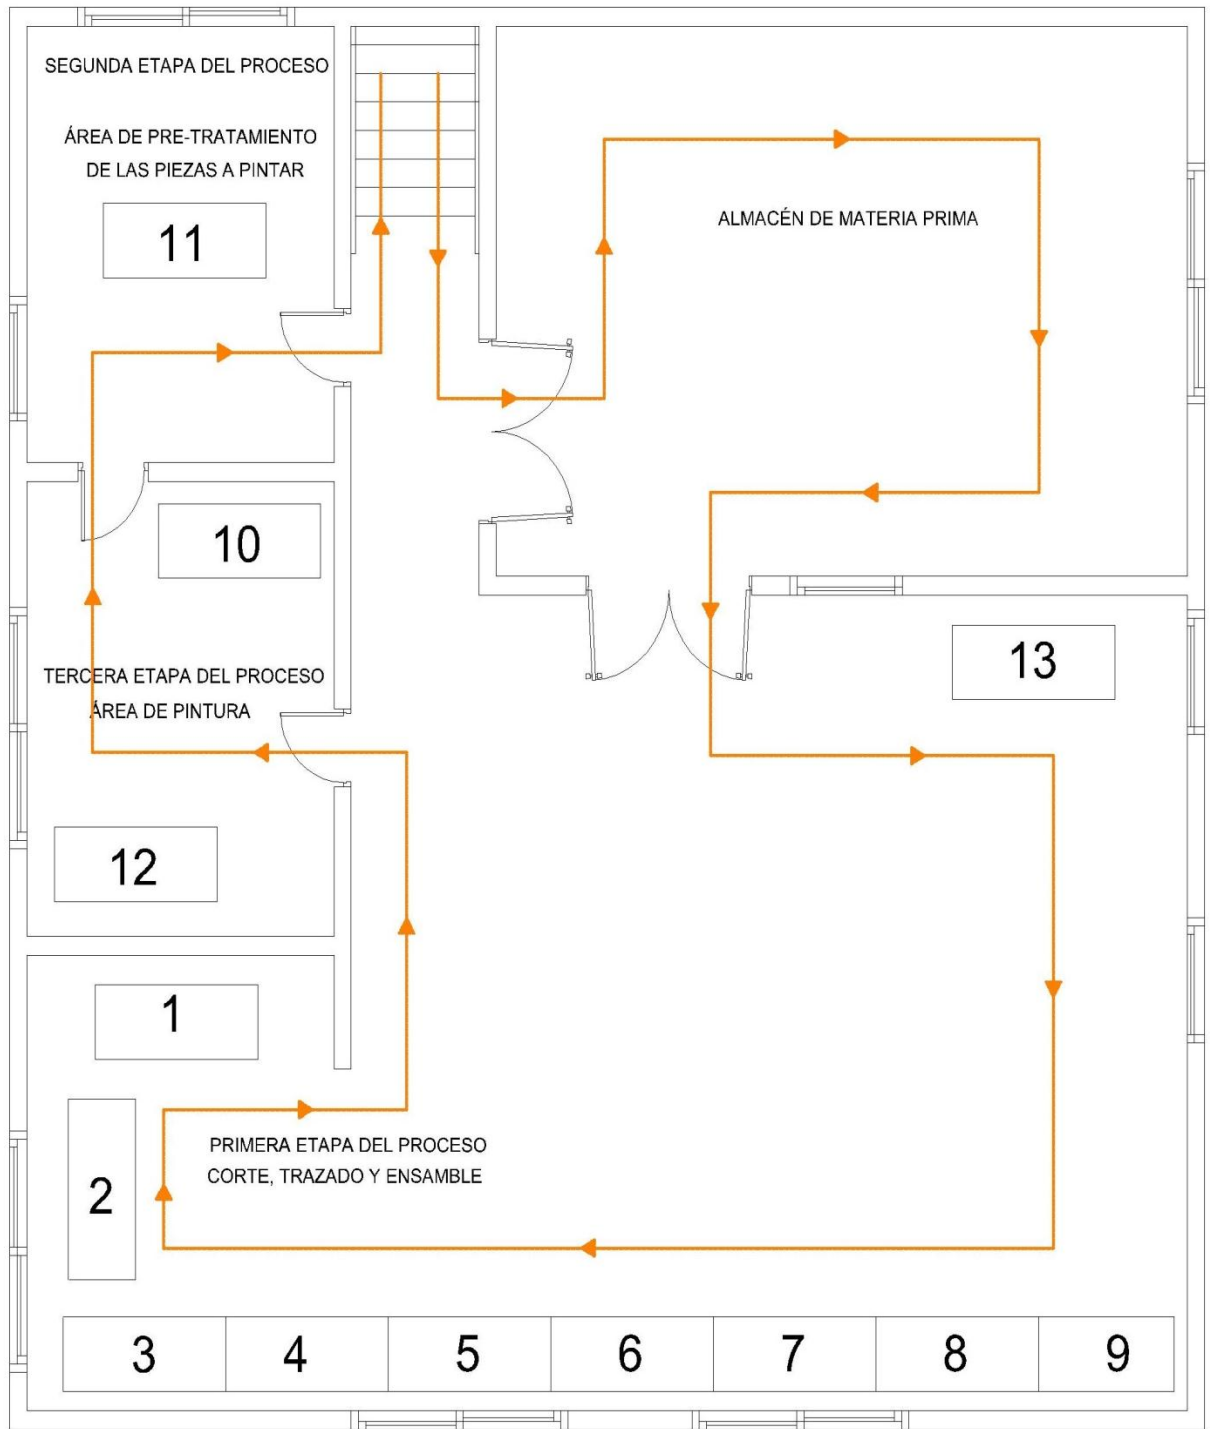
Plano: Recorrido en planta alta del encargado/supervisor del laboratorio de control de calidad.
